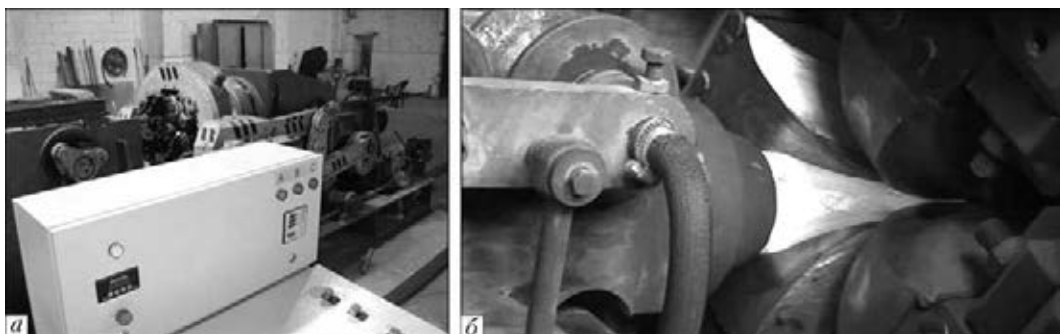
Стан СШ175 (а) и процесс прокатки (б)
